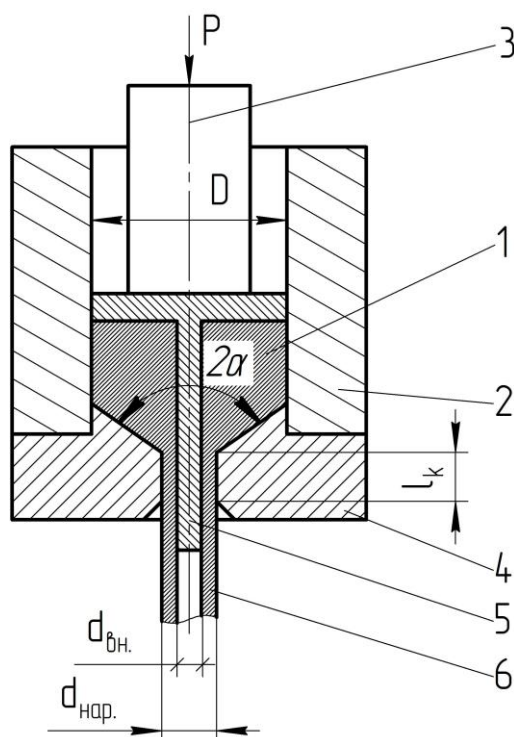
Схема процесу пресування труби: 1 - метал; 2 - контейнер; 3 - пуансон; 4 - матриця; 5 - оправка; 6 - труба .
